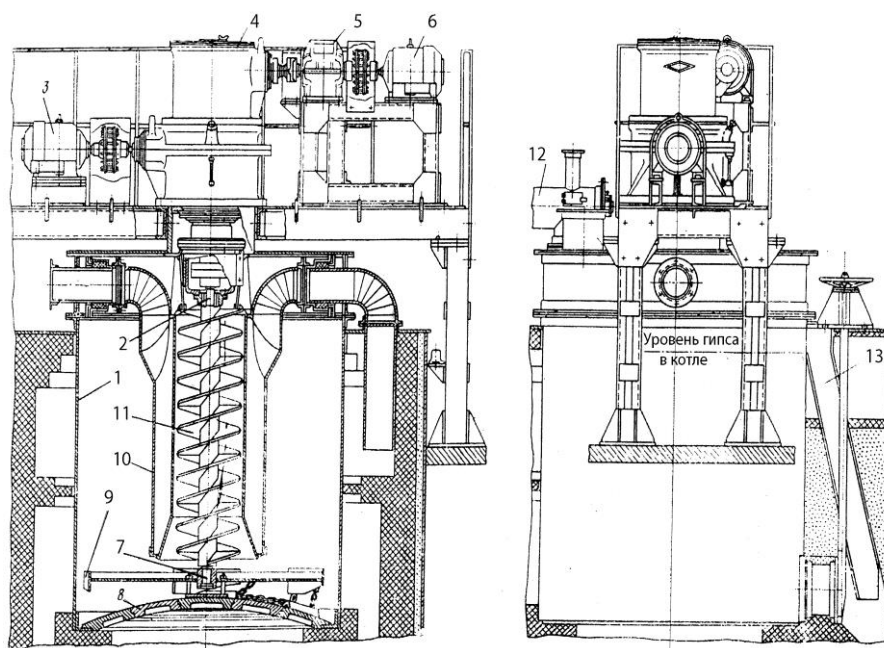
Котёл гипсоварочный СМА 158 А (внешний вид)
